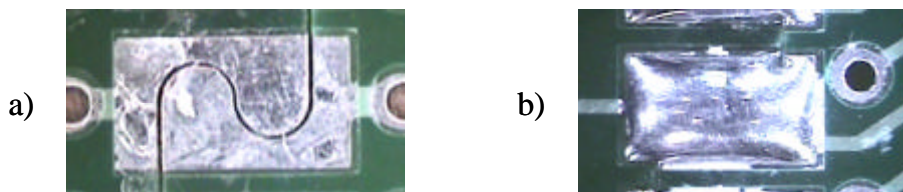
Detalle de la soldadura de dos contactos
